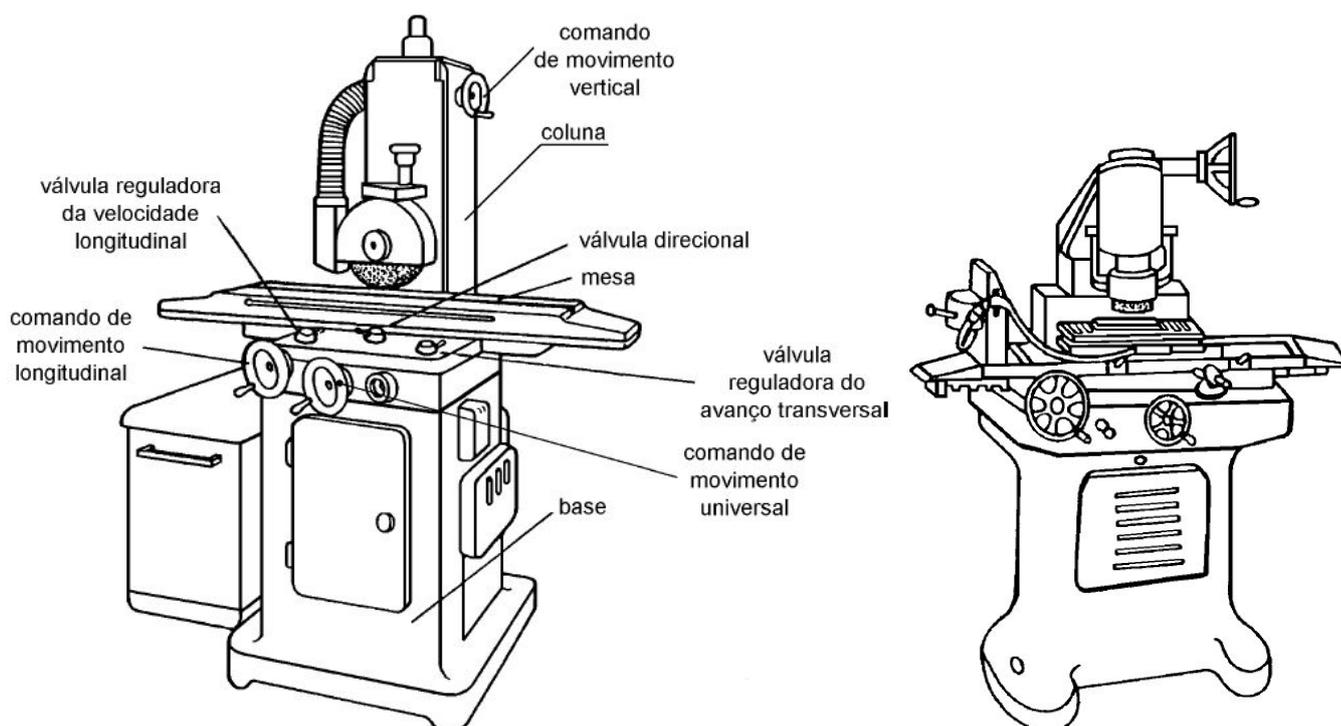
Retificadora plana tangencial e plana vertical. Fonte - SENAI
